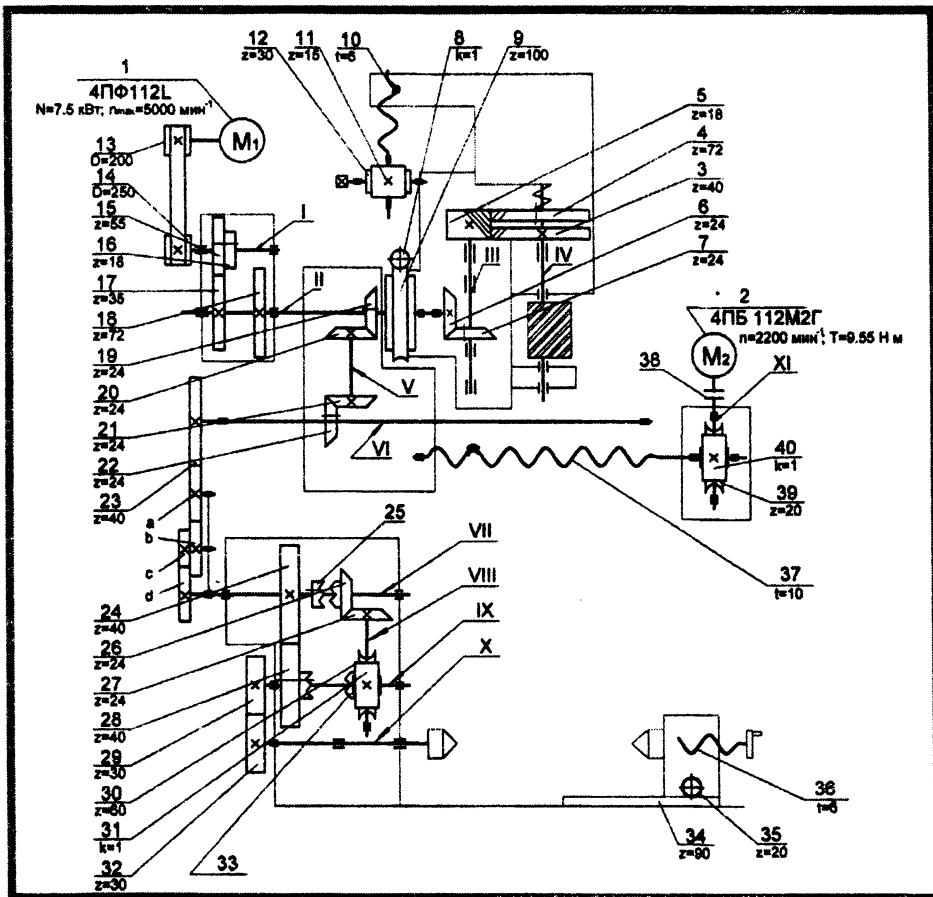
Кинематическая схема станка для обработки профильных деталей машин
